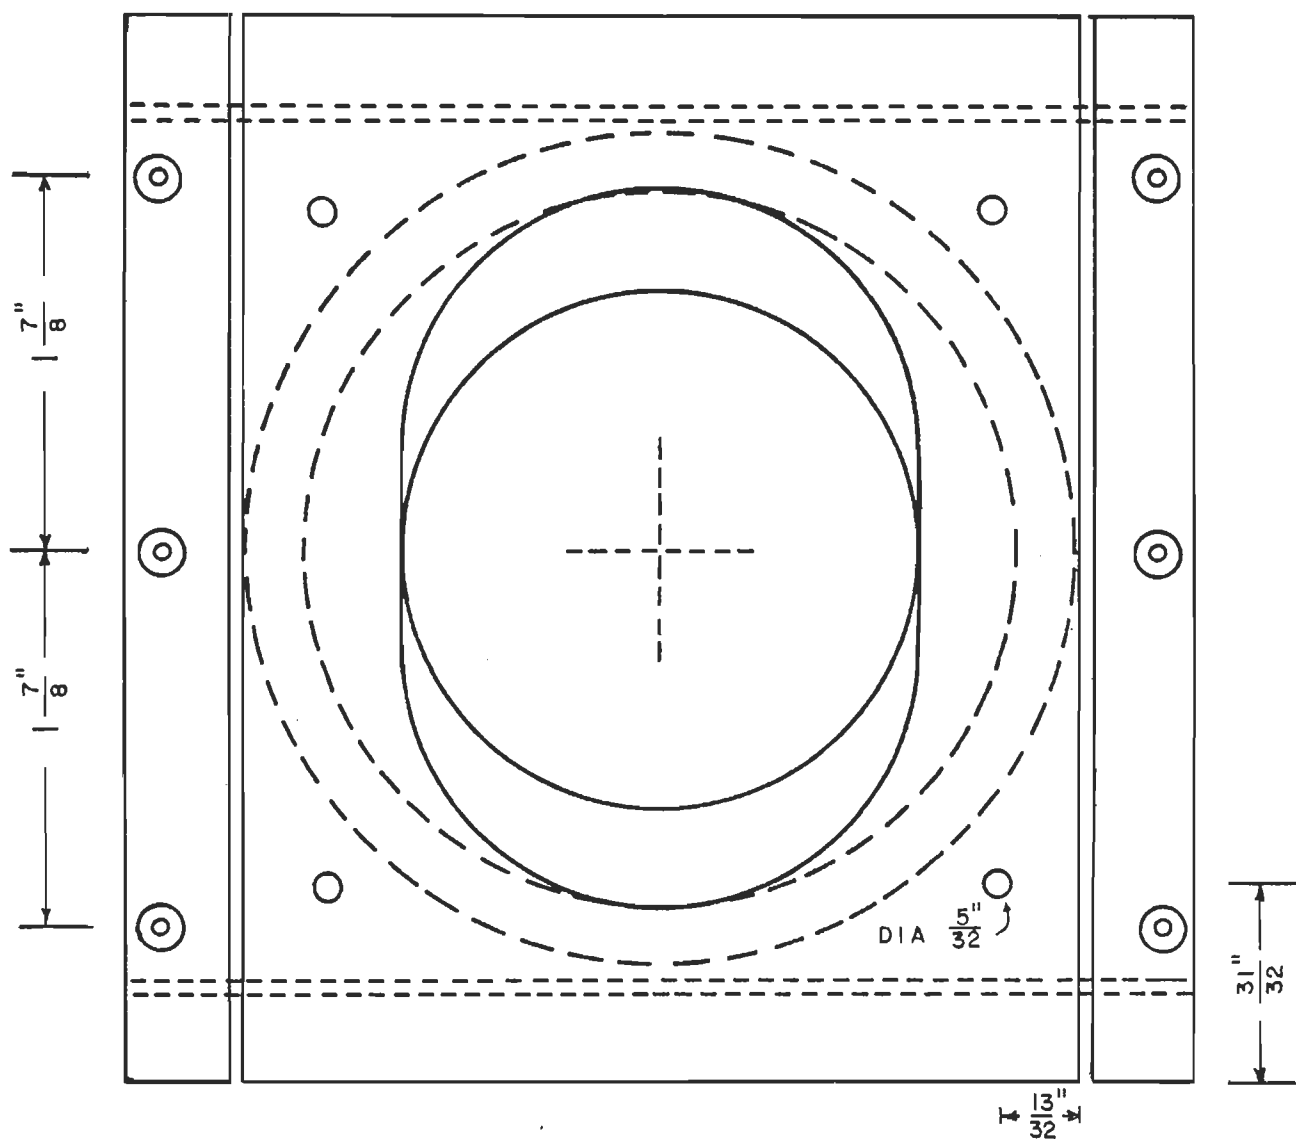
Plan détaillé de la section c vue dans un plan horizontal inférieur.
